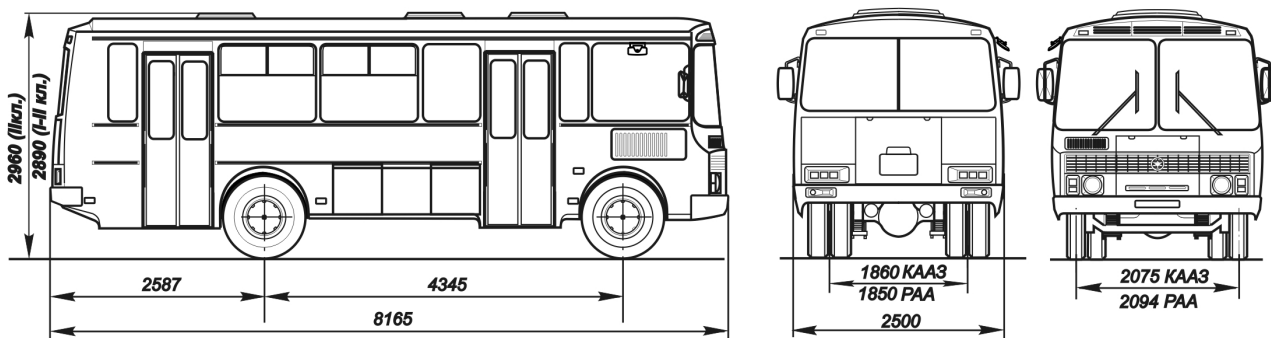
Габаритные размеры автобуса ПАЗ-4234
